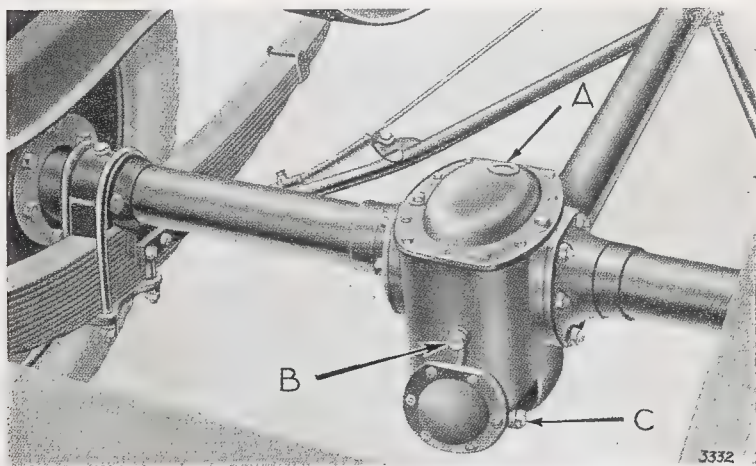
Vue du pont arrière. A) Bouchon de remplissage;
